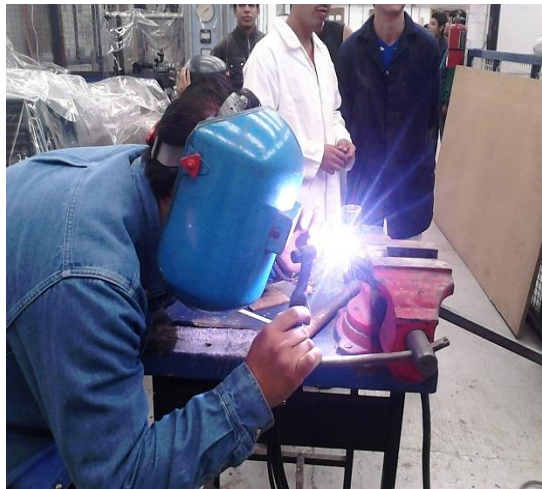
roceso de soldadura del codo y cople nuevo.
